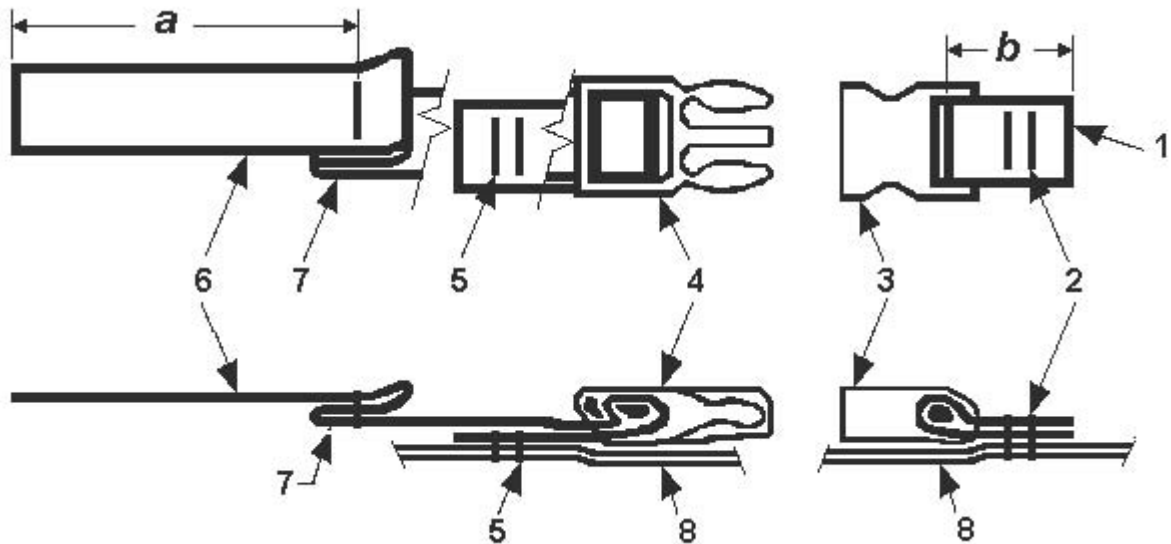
Conjunto de tira pectoral (parte ajustable izquierda y parte fija derecha)
